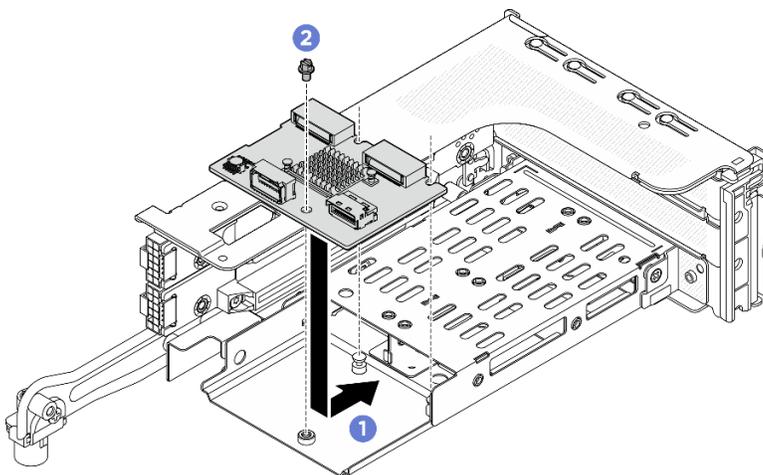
Installation du fond de panier M.2 dans le boîtier de carte mezzanine M.2 3FH
